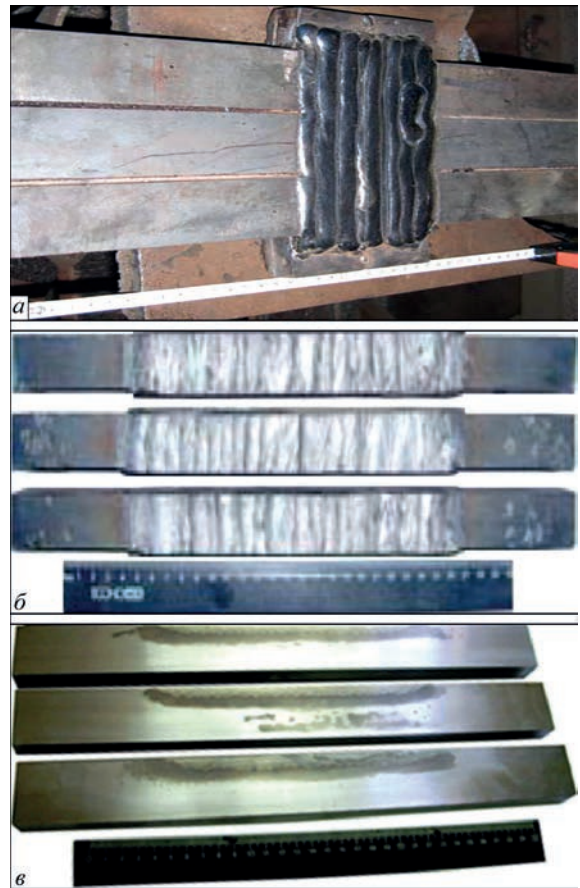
Пакет заготовок після наплавлення (а), заготовки зразків після розрізання (б), зразки після остаточного шліфування (в)
